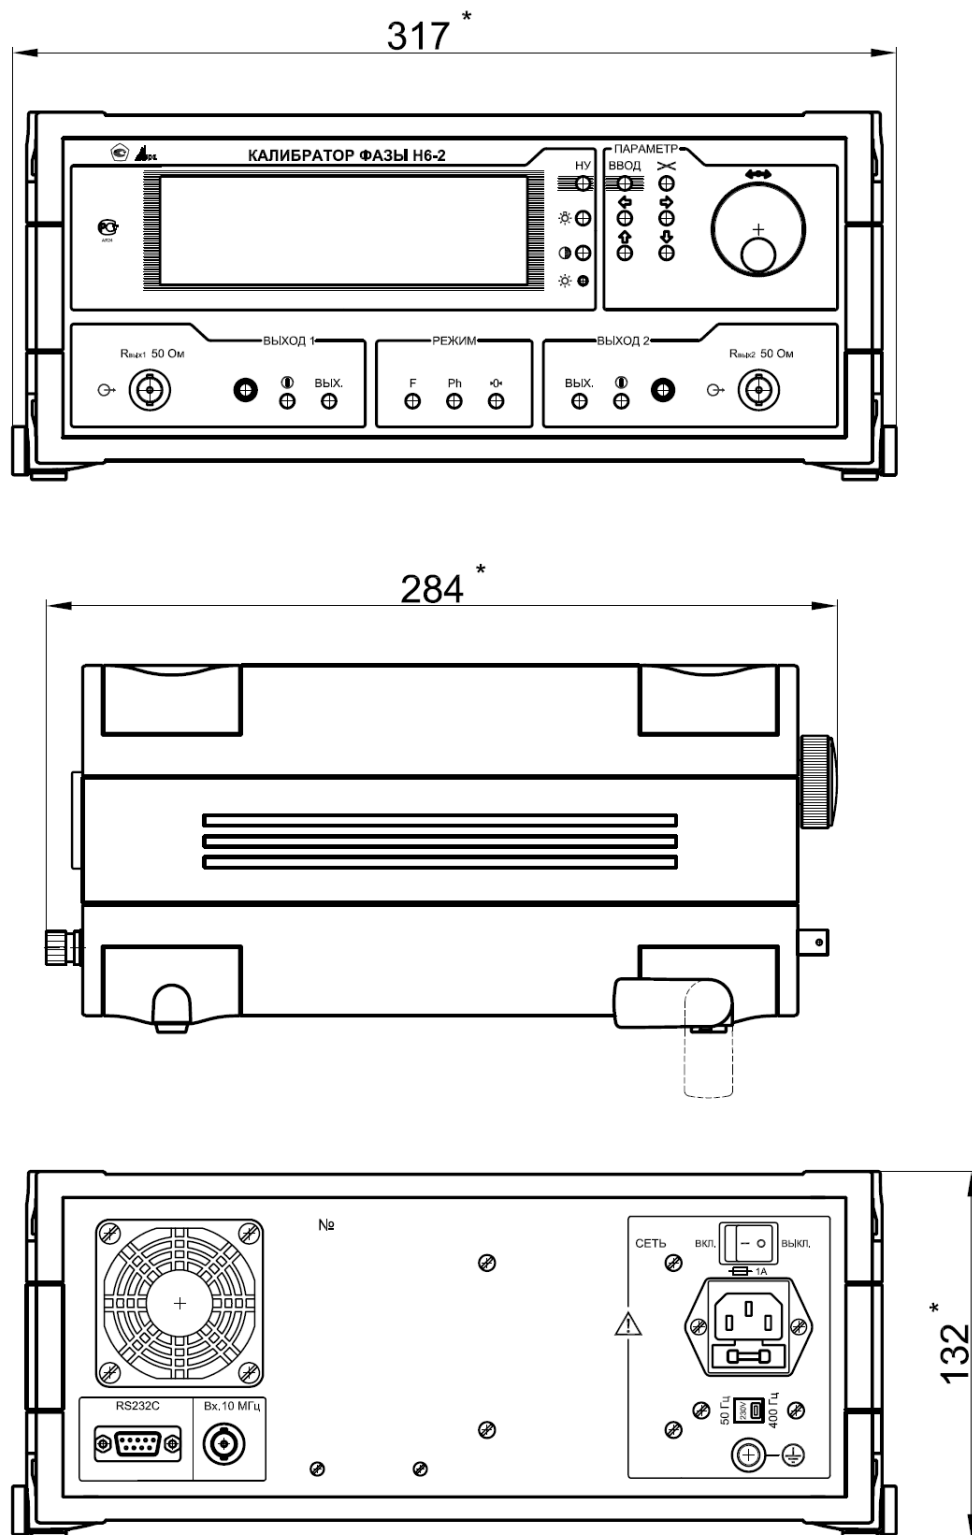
Общий вид калибратора Н6-2 и его габаритные размеры
